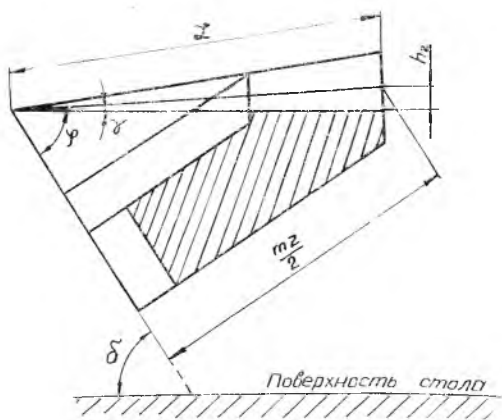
Схема установки конического колеса при фрезеровании зуба
